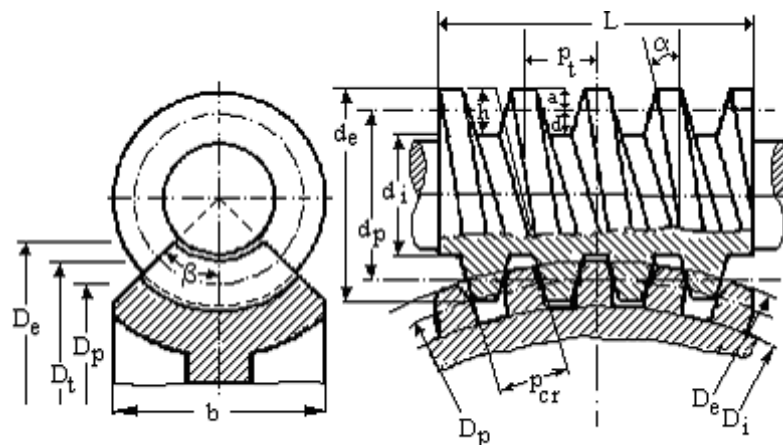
Nomenclatura de engranaje de tornillo sin-fín.
